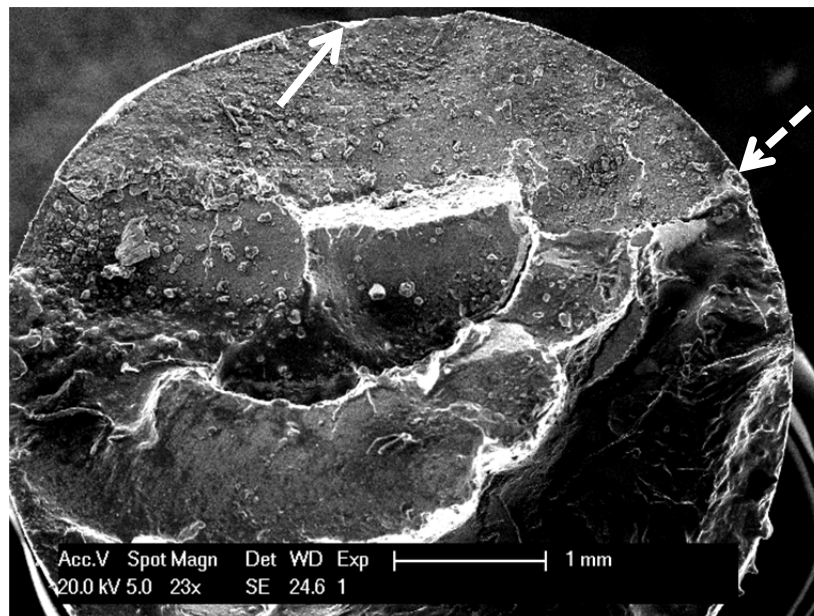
REM Aufnahme Ermüdungsbruch Außendraht (Pfeil: Rissinitiierung; strichlierter Pfeil: Übergang Ermüdungsbruchfläche / Restgewaltbruchfläche)
